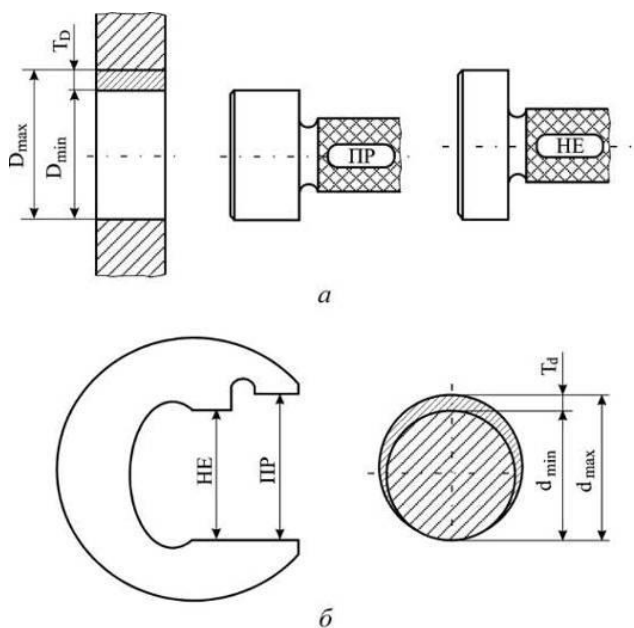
Схемы контроля гладкими предельными калибрами отверстия (а) и вала (б)
